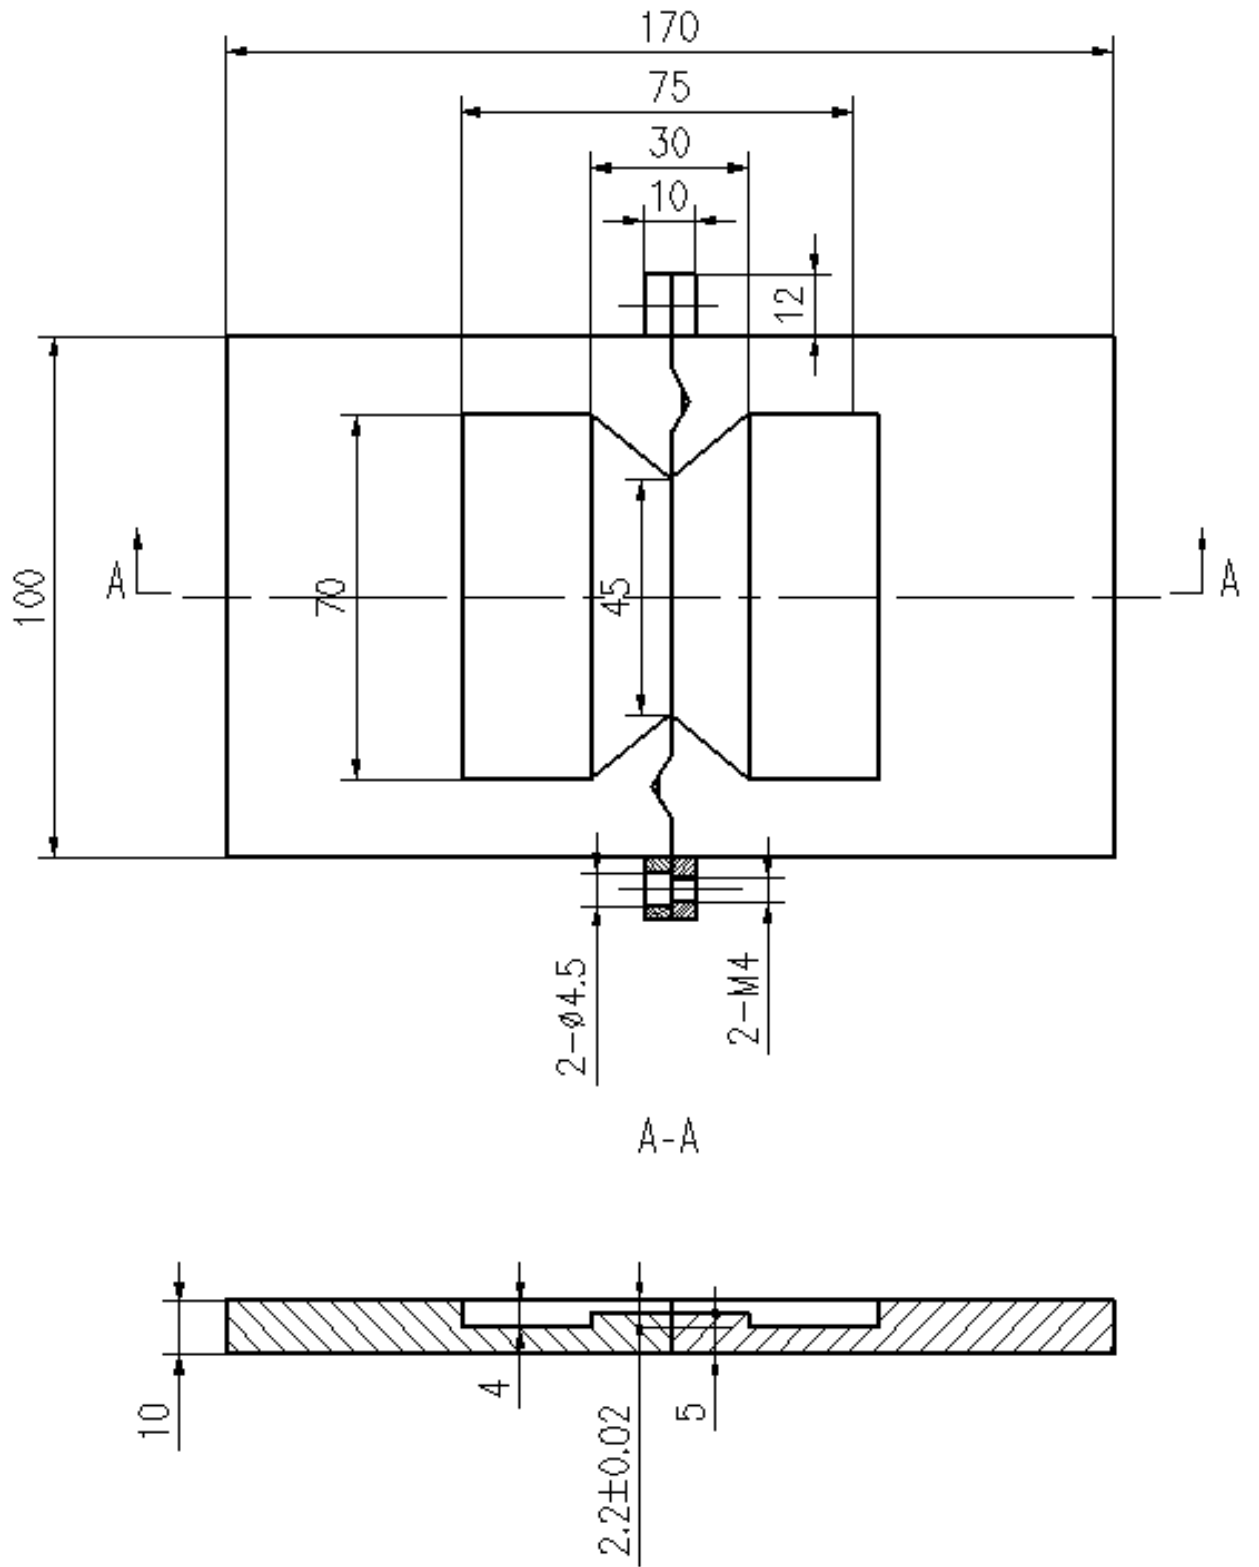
道路交通标线材料抗开裂性测试仪制样模具结构尺寸图
